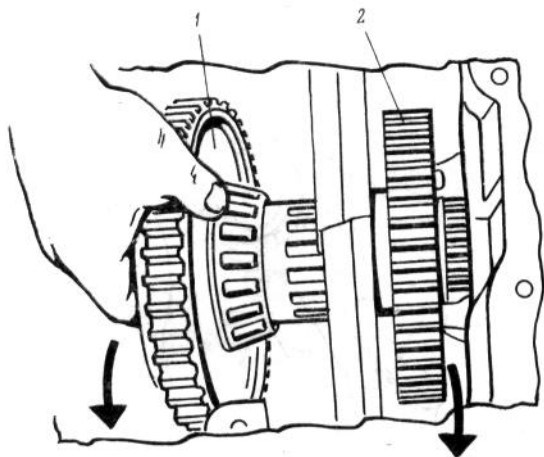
Знімання вторинного вала: 1- вторинний вал; 2- ведена шестерня II ступені редуктора
